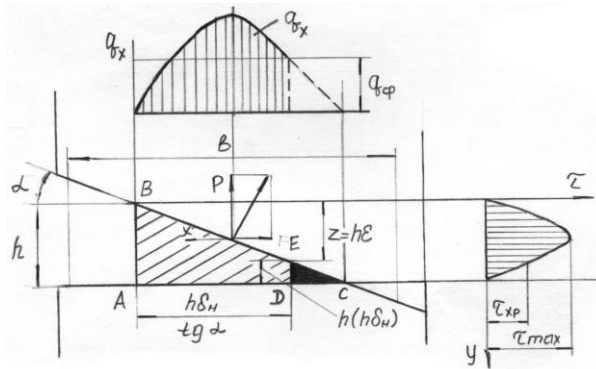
Схема різання металу на ножицях з похилими ножами
